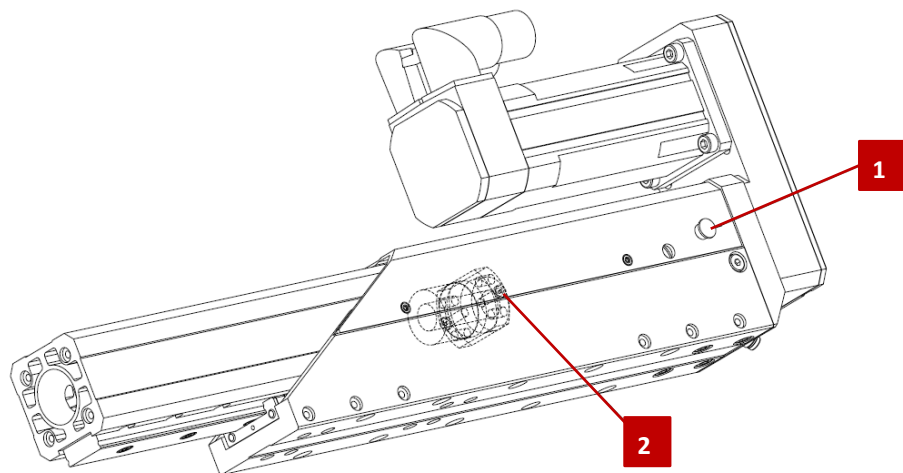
Spindelausleger – Schmiernippel Spindelgetriebe
